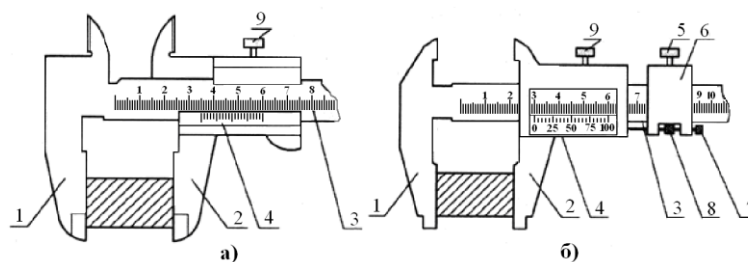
Визначення розміру за допомогою штангенциркуля
